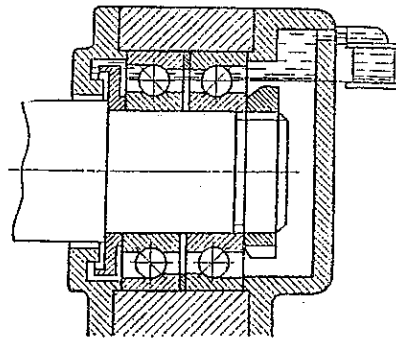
Сливное отверстие в крышке корпуса тихоходного подшипника
